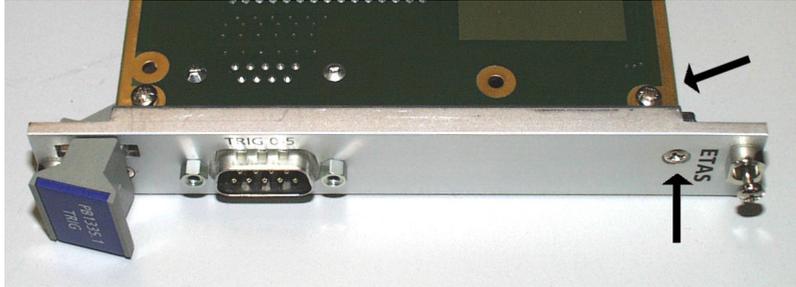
Schrauben für die obere Frontplattenbefestigung
